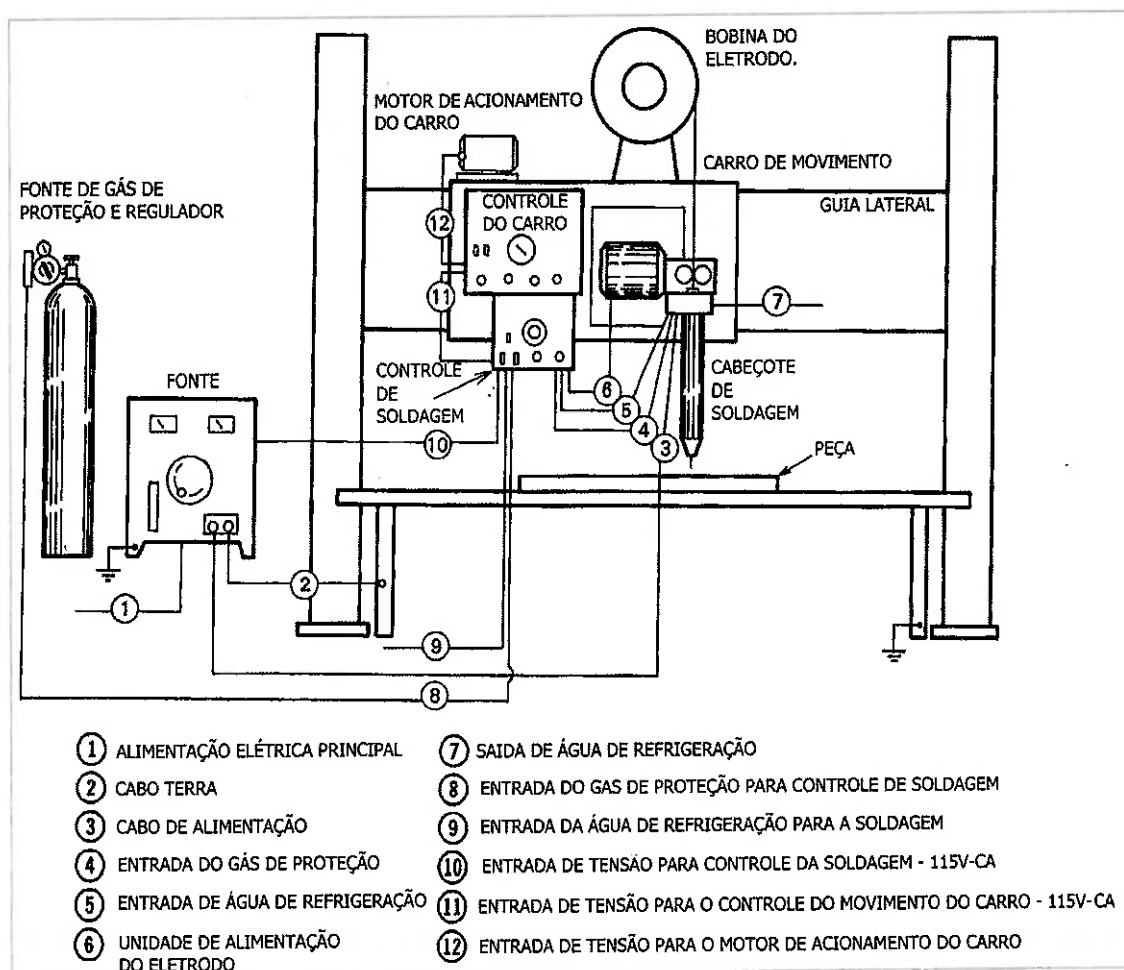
Soldagem arame tubular auto-protegido (Modif. de [8]).
